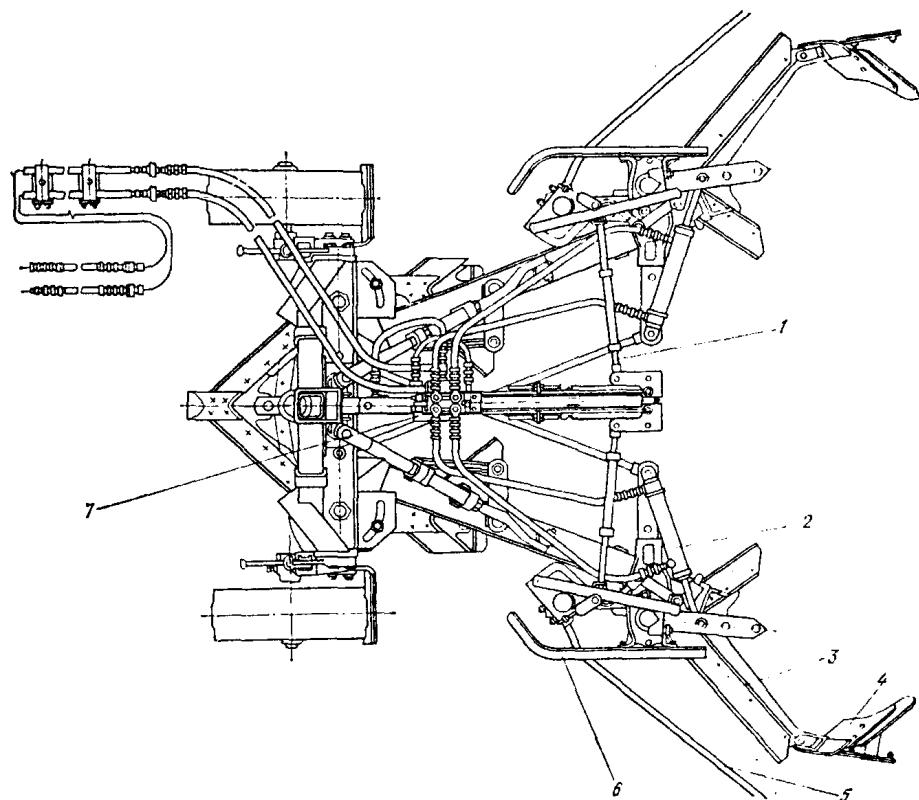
Схема приспособления ПРВМ-11.000:
